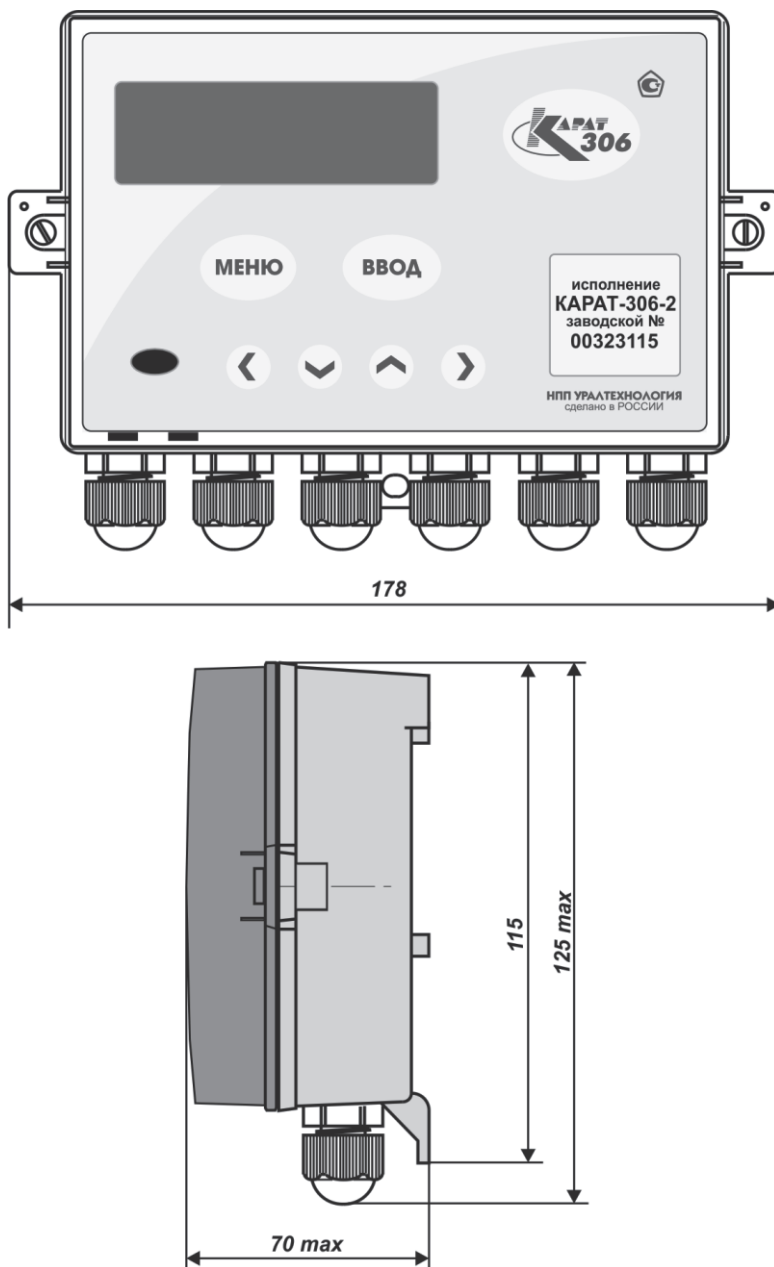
Габаритные размеры вычислителя KARAT-306
